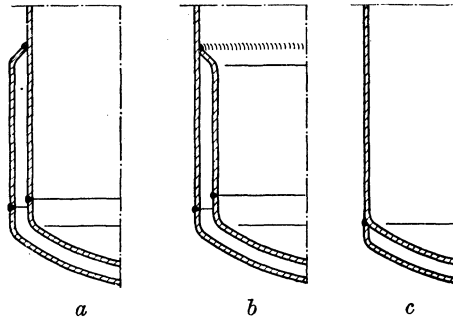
Schweißnähte an Doppelböden.
